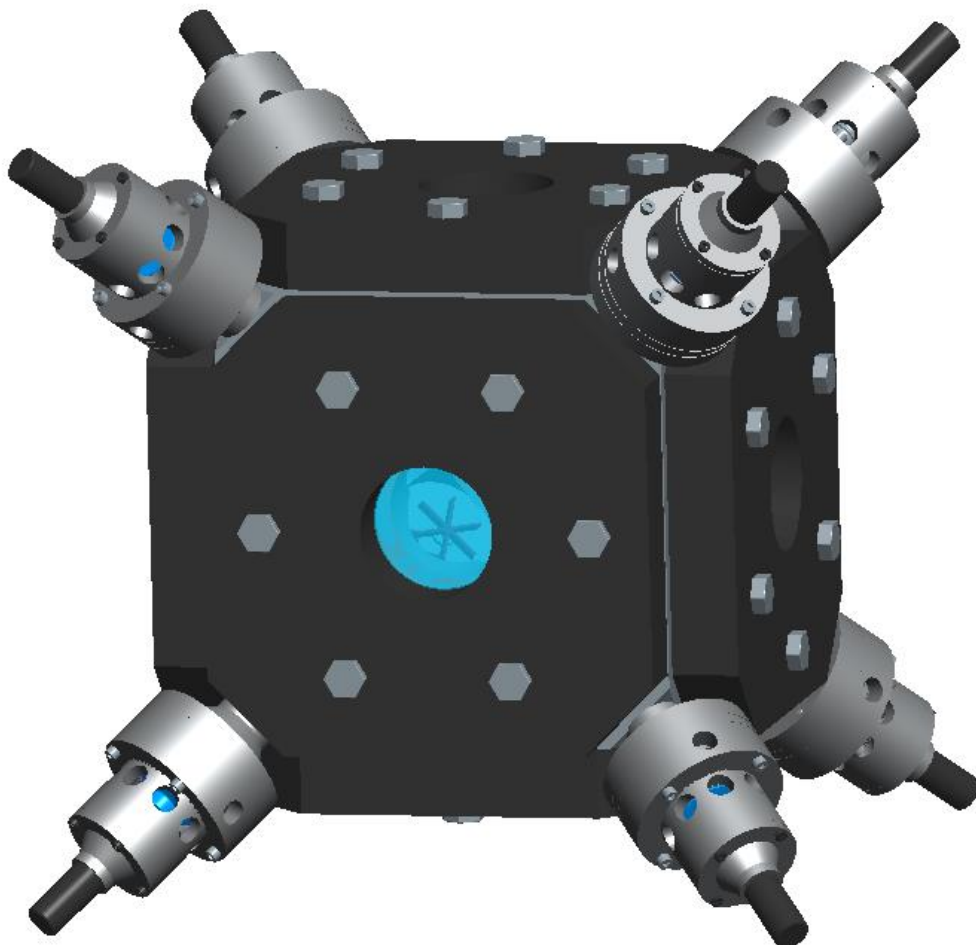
Der Explosionswürfel mit eingebauten Turbulenzerzeugern
